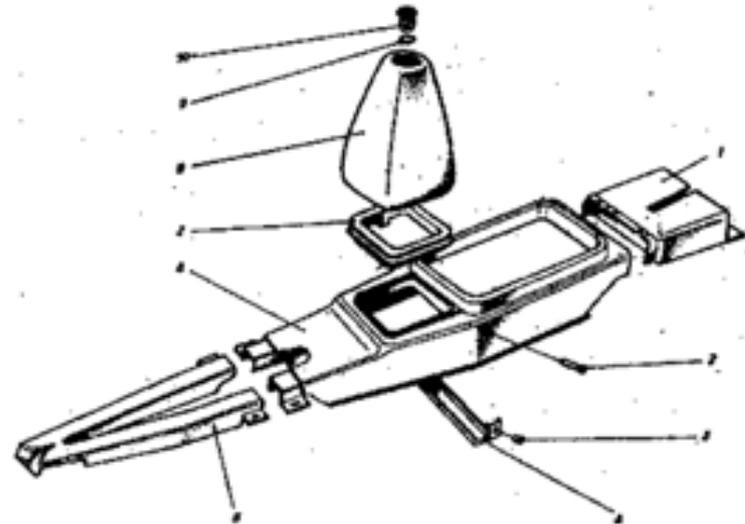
Воздуховоды: 1 - накладка передняя; 2 - поршень; 3 - втулка; 4 - кронштейн; 5 - накладка задняя; 6 - накладка средняя; 7 - крышка чехла; 8 - чехол рычага; 9 - кольцо чехла; 10 - втулка чехла.
